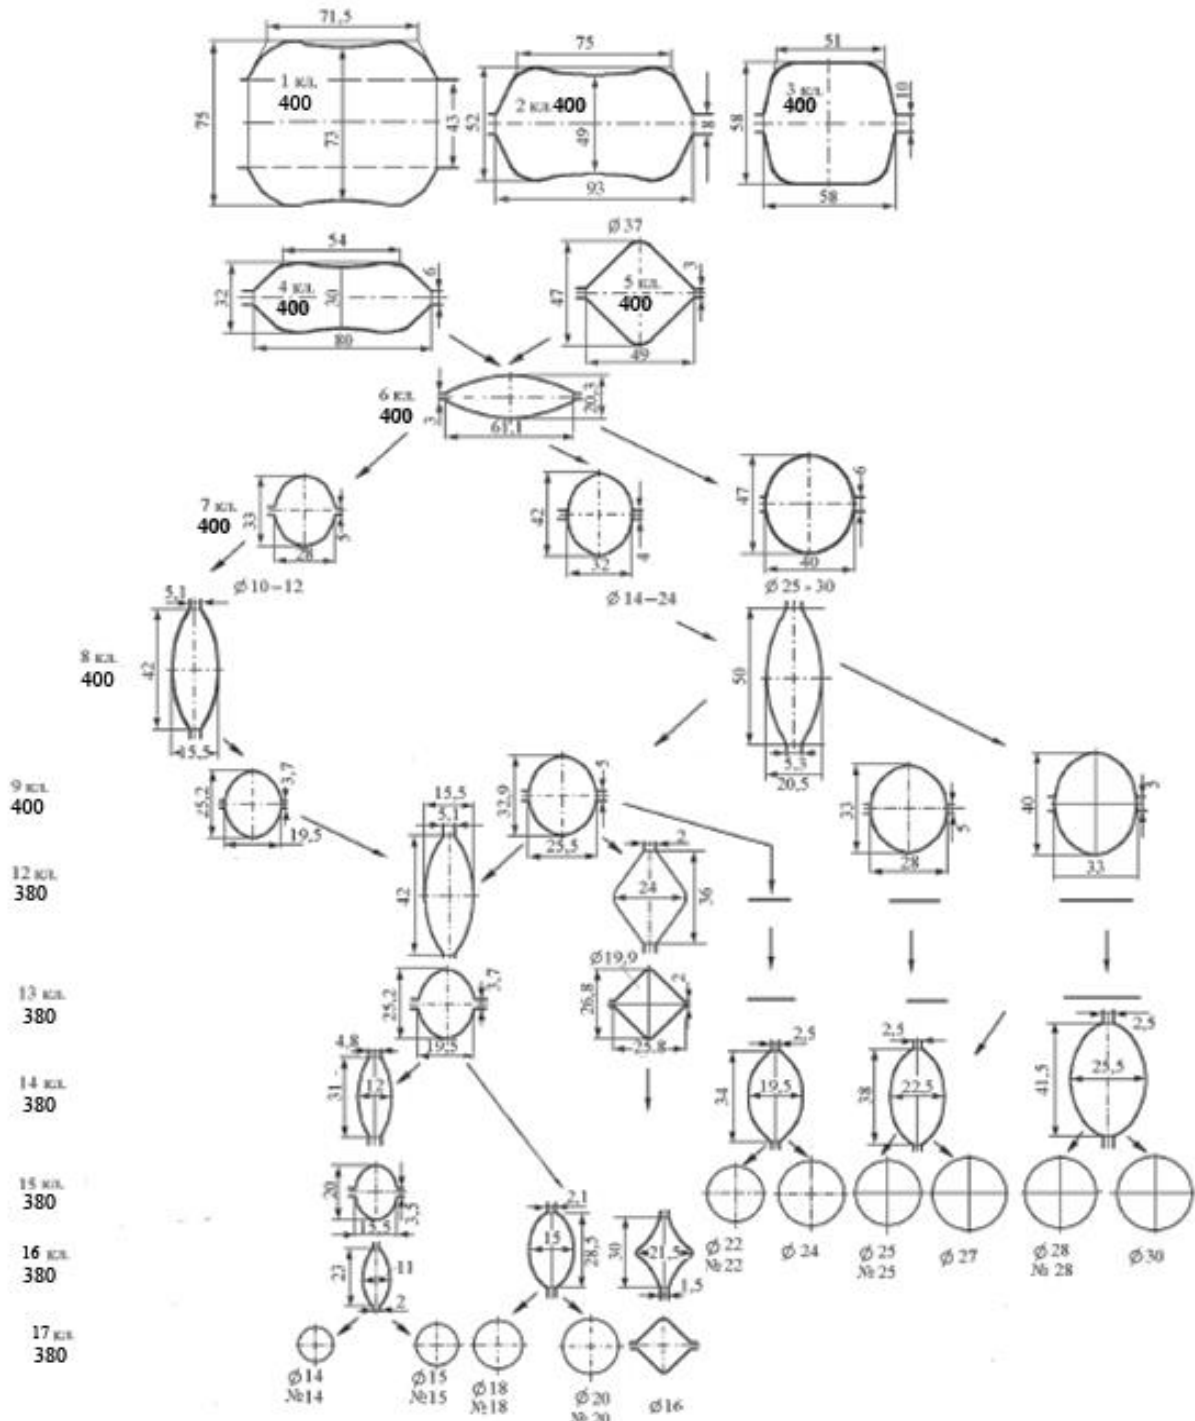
Калибровка валков мелкосортного непрерывного стана
